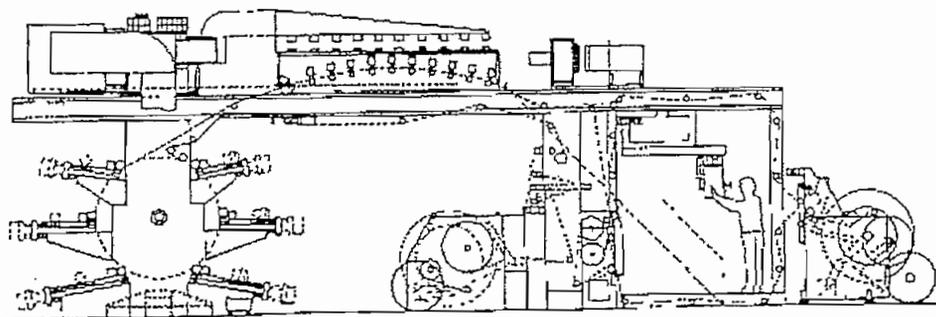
Máquina impresora de seis colores (ref. 12)
